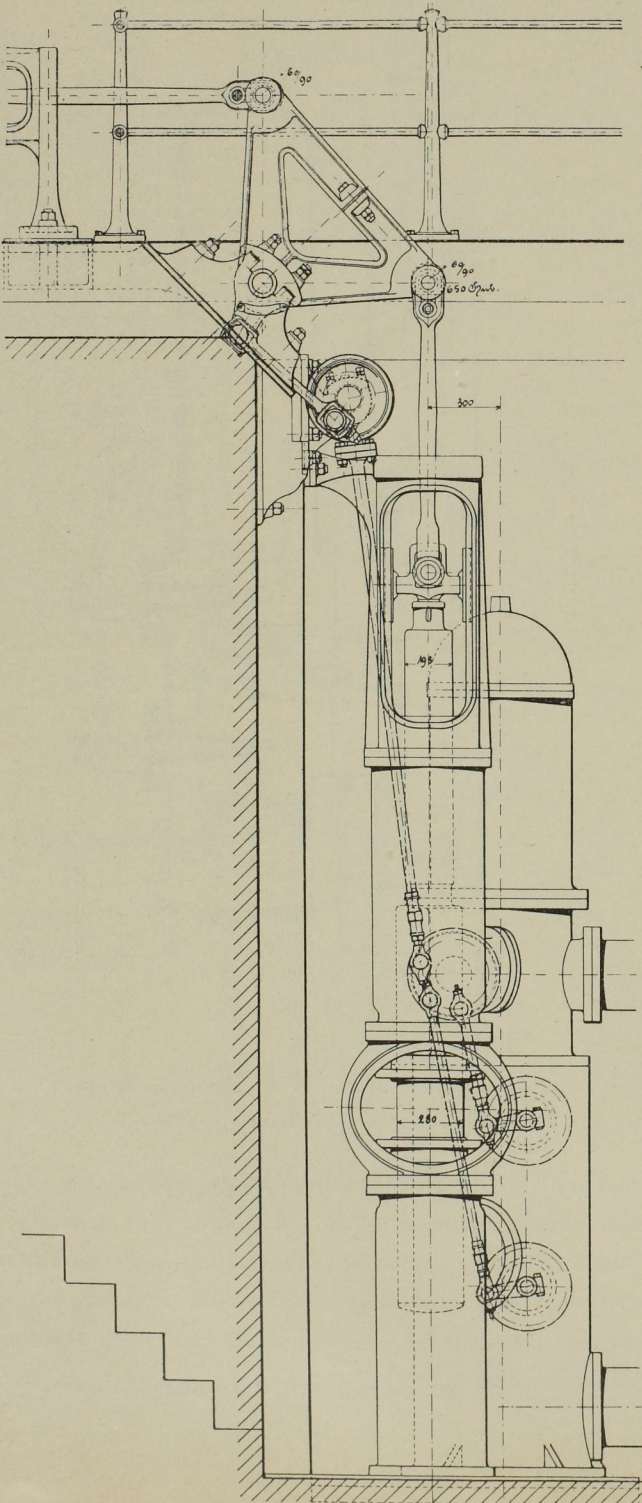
Seitenansicht der Druckpumpe. Masst. 1 : 30.
